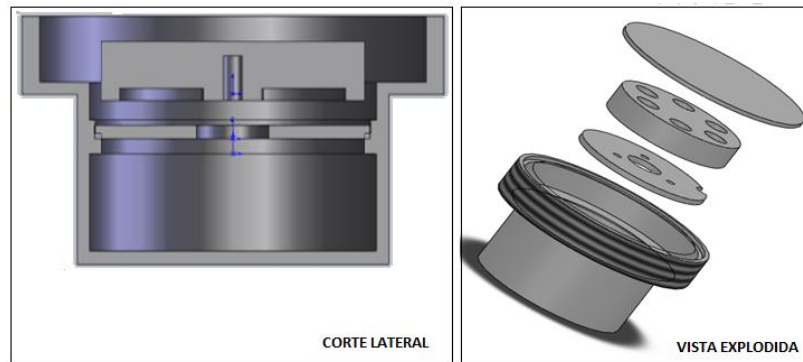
Montagem de peças, ao lado esquerdo a vista em corte, ao direito a vista explodida.
